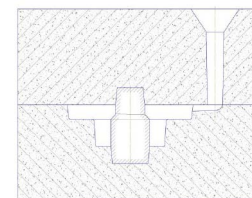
Вариант формовки с вертикальным расположением стержня
